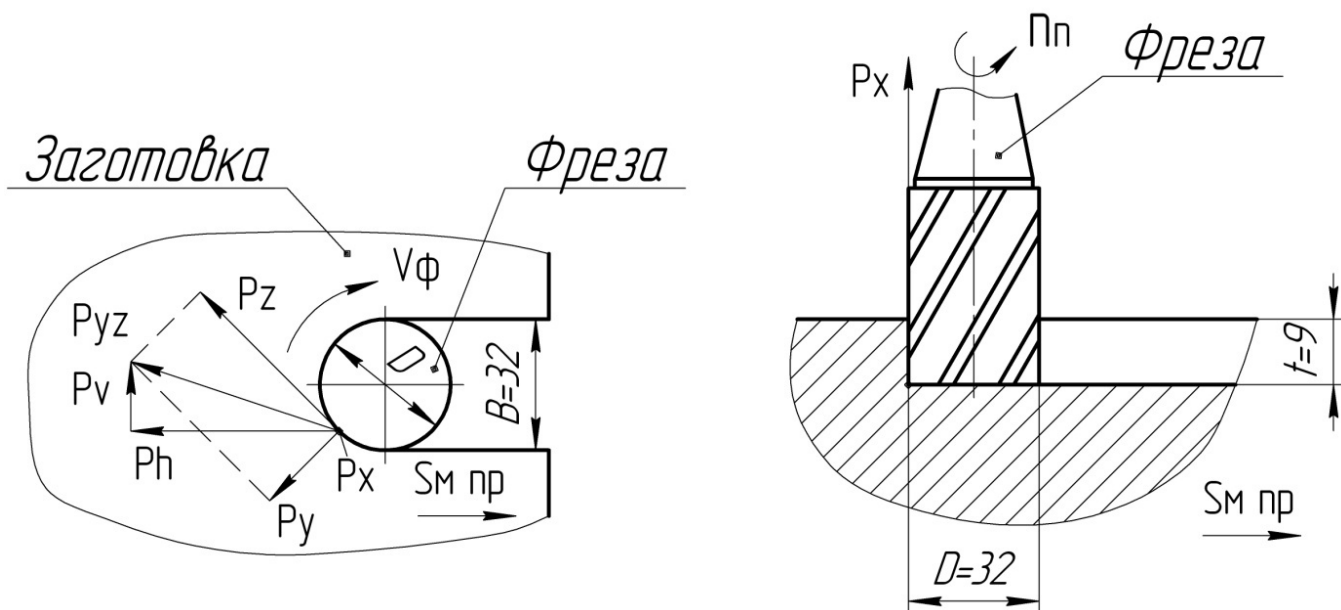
Сили різання при фрезеруванні шпонковою фрезою
